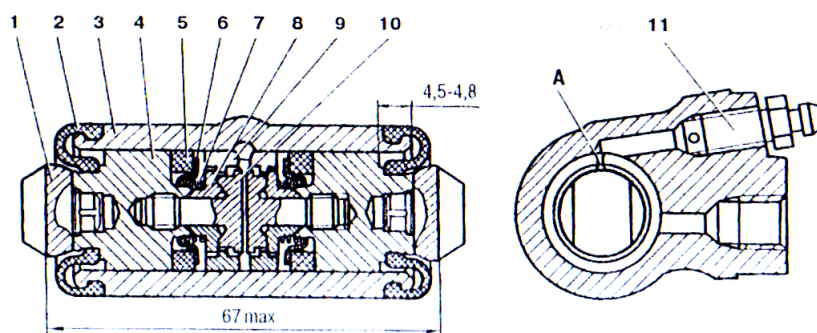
Схема заднего рабочего тормозного цилиндра автомобиля ВАЗ-2107
